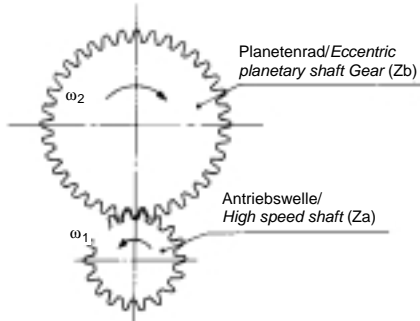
Stirnradverzahnung/ *Involute gearing
